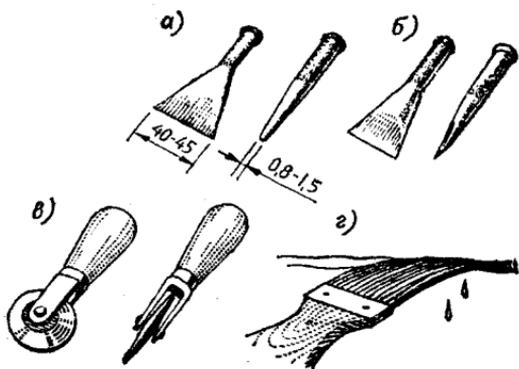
Инструмент для конопатки: а — лебеза для осаживания конопатки в пазу; б — лебеза для разладки пазов; в — диск для конопатки тонкой обшивки; г — окраска паза флейцем.
